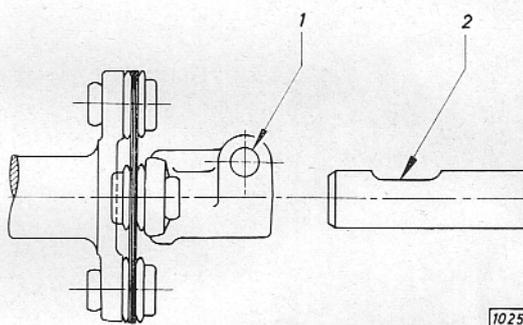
Lage der Lenkspindel zum Lenkspindelflansch
